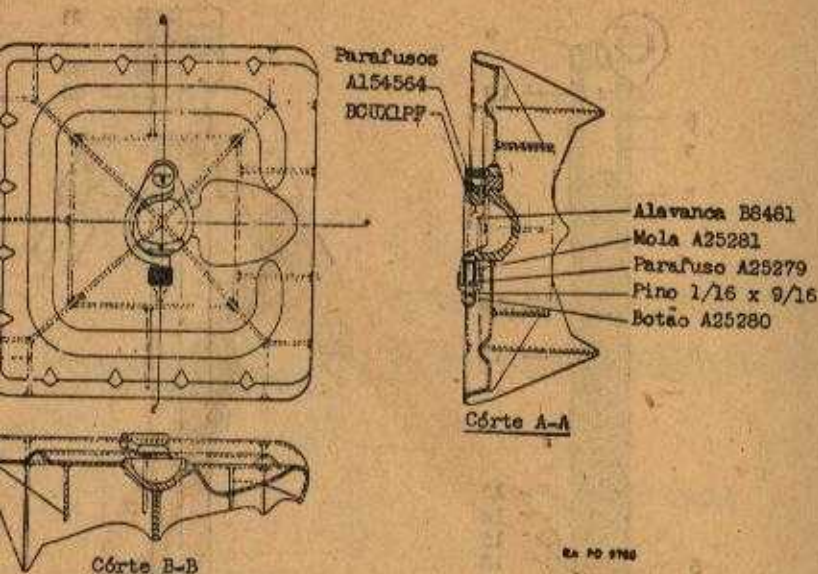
Placa-base do Morteiro 60 mm — Vista detalhada
